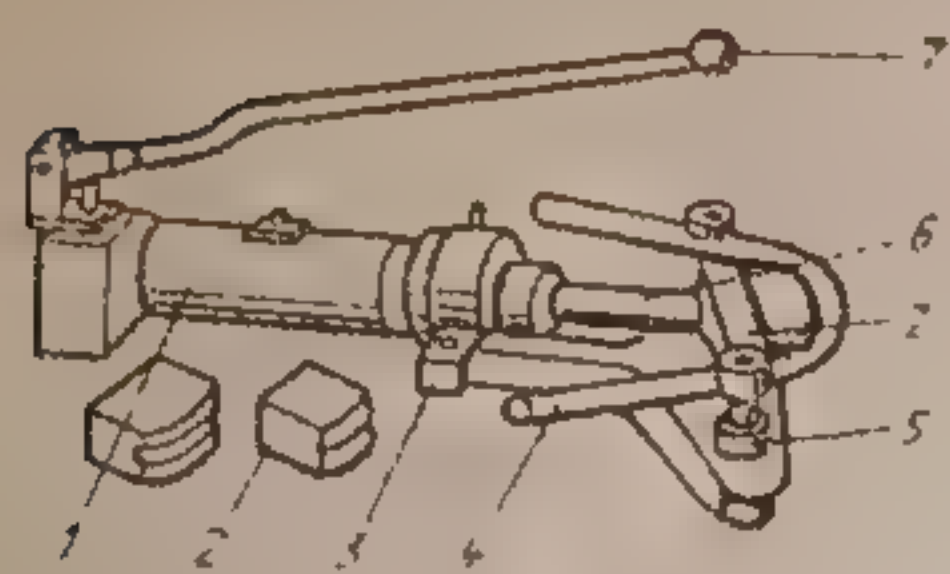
Трубогиб с гидроприводом: 1 — гидроцилиндр; 2 — сменные колодки; 3 — основание; 4 — изгибаемая труба; 5 — упоры-ролики; 6 — плунжер; 7 — рукоятка
